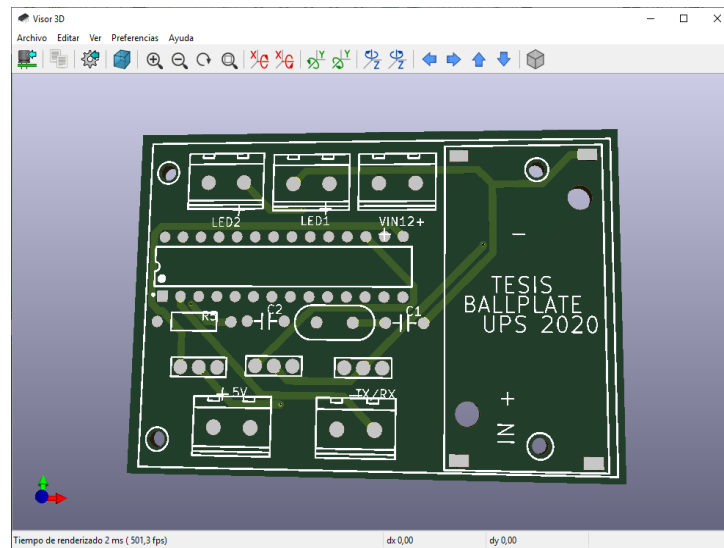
Visualización del Diseño en 3d en Kicad de tarjeta PCB. Autores.
